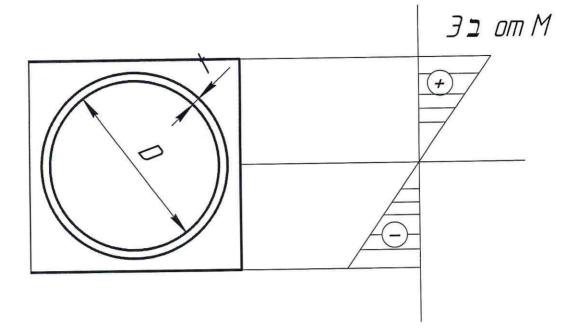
Эпюра изгибающего момента в месте сварного шва
